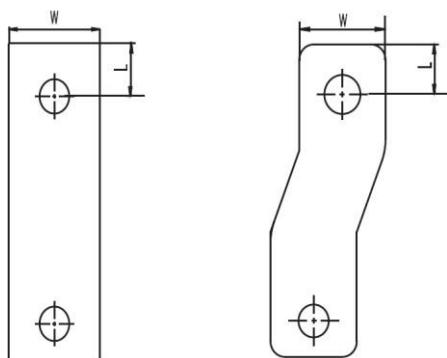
Габаритные и установочные размеры ручки на дверь шкафа, мм
